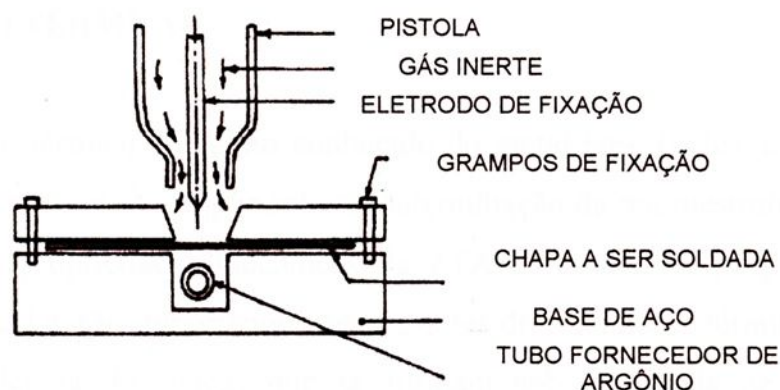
Dispositivo para soldagem TIG (Mohandas & Madhusudan, 1997).
